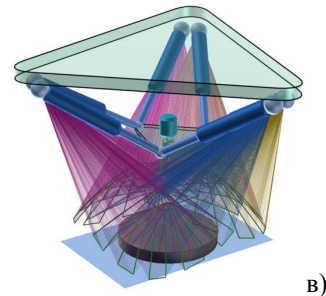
Моделювання обробки фрезеруванням конічної поверхні по спіралі верстатом- гексаподом:
